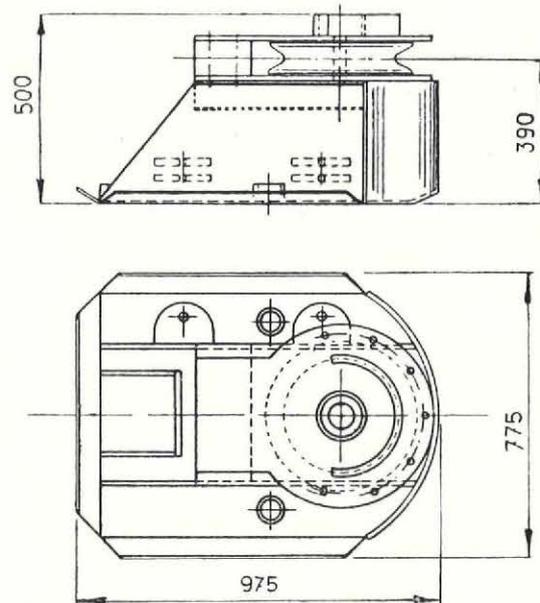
Poulie de renvoi sur bâti indépendant (élévation et plan).
